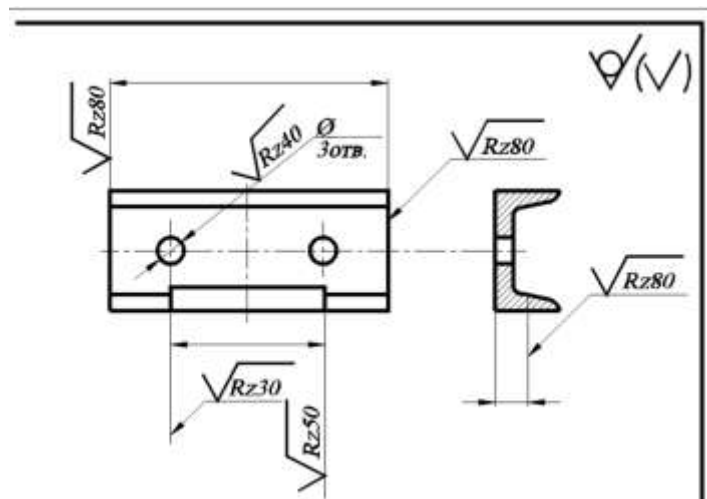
Указание шероховатости, когда большая часть поверхностей не обрабатывается
